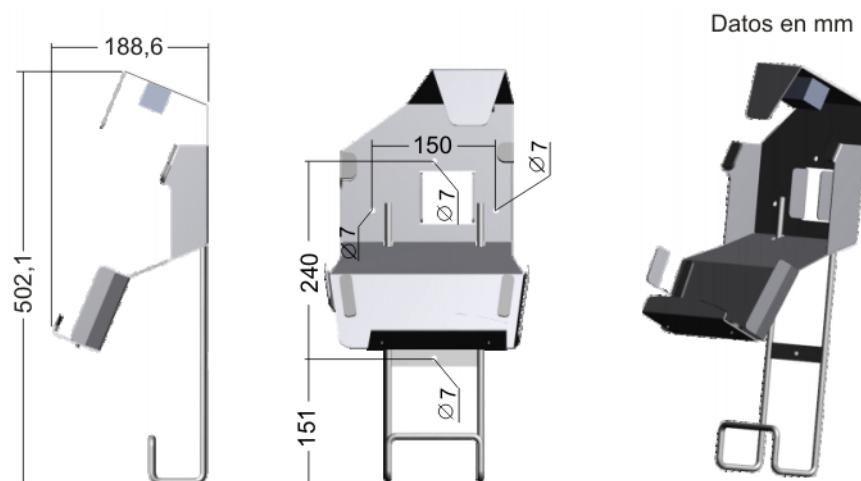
Medidas y cotas de barrenado para el soporte del smartPAD
